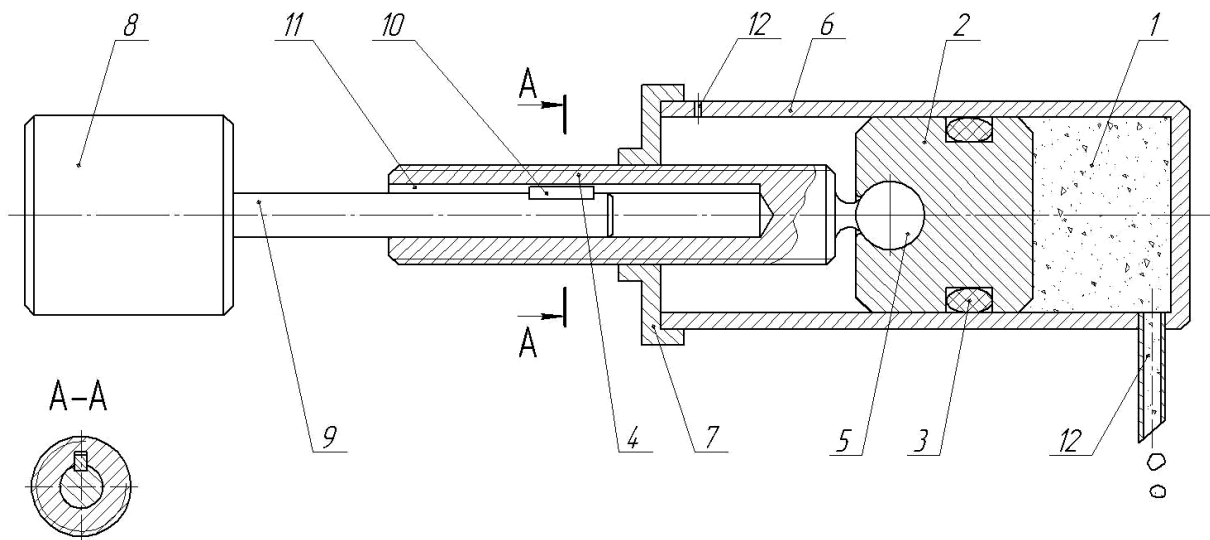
Конструкція краплинного дозатора для уведення присадок
